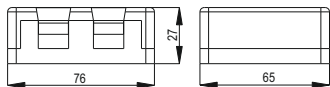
Корпус CS2-022 / Figure 5 – CS2-022 housing
